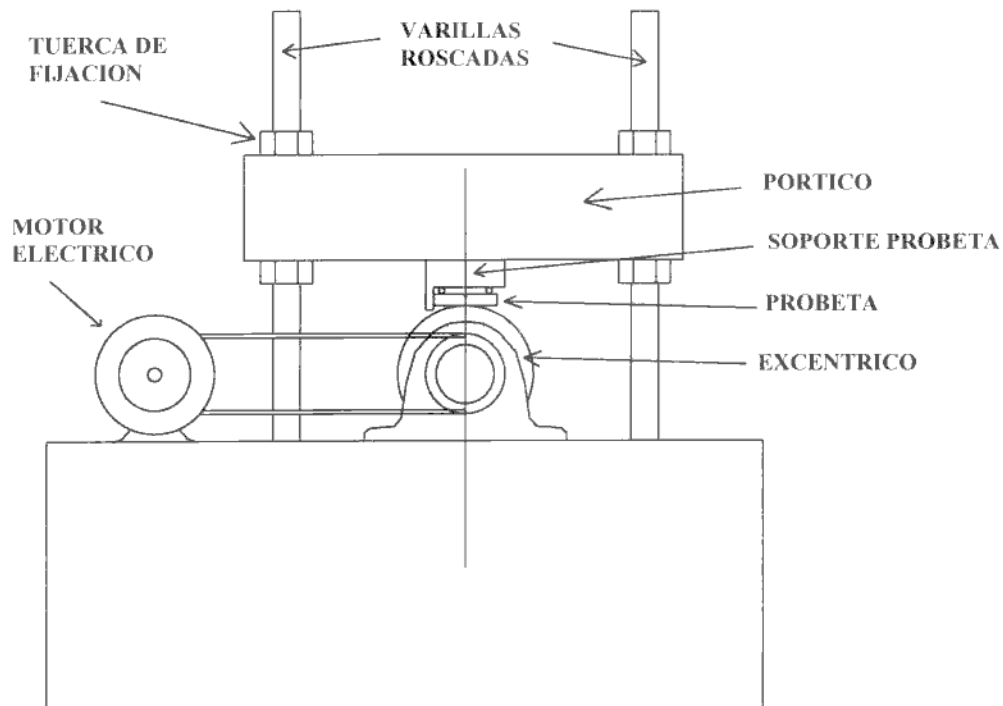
Dispositivo de prefisurado (LEMIT)
